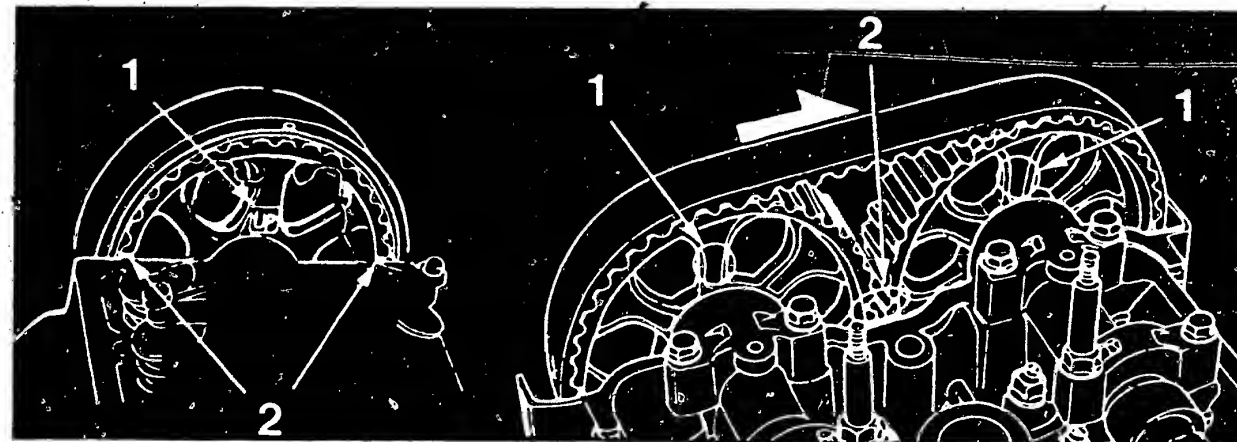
Ausrichtung der Nockenwellenräder zur Einstellung des Ventilspiels des ersten Zylinders. 1 «UP»-Markierung, 2 Nuten. Links: EW3-, rechts: ZC1-Motor.
